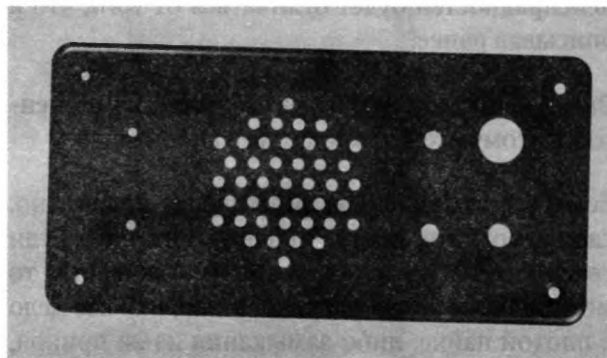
Внешний вид панели после сверления. Отверстия можно аккуратно просверлить с помощью небольшой переносной аккумуляторной дрели, если точно наметить их центры
